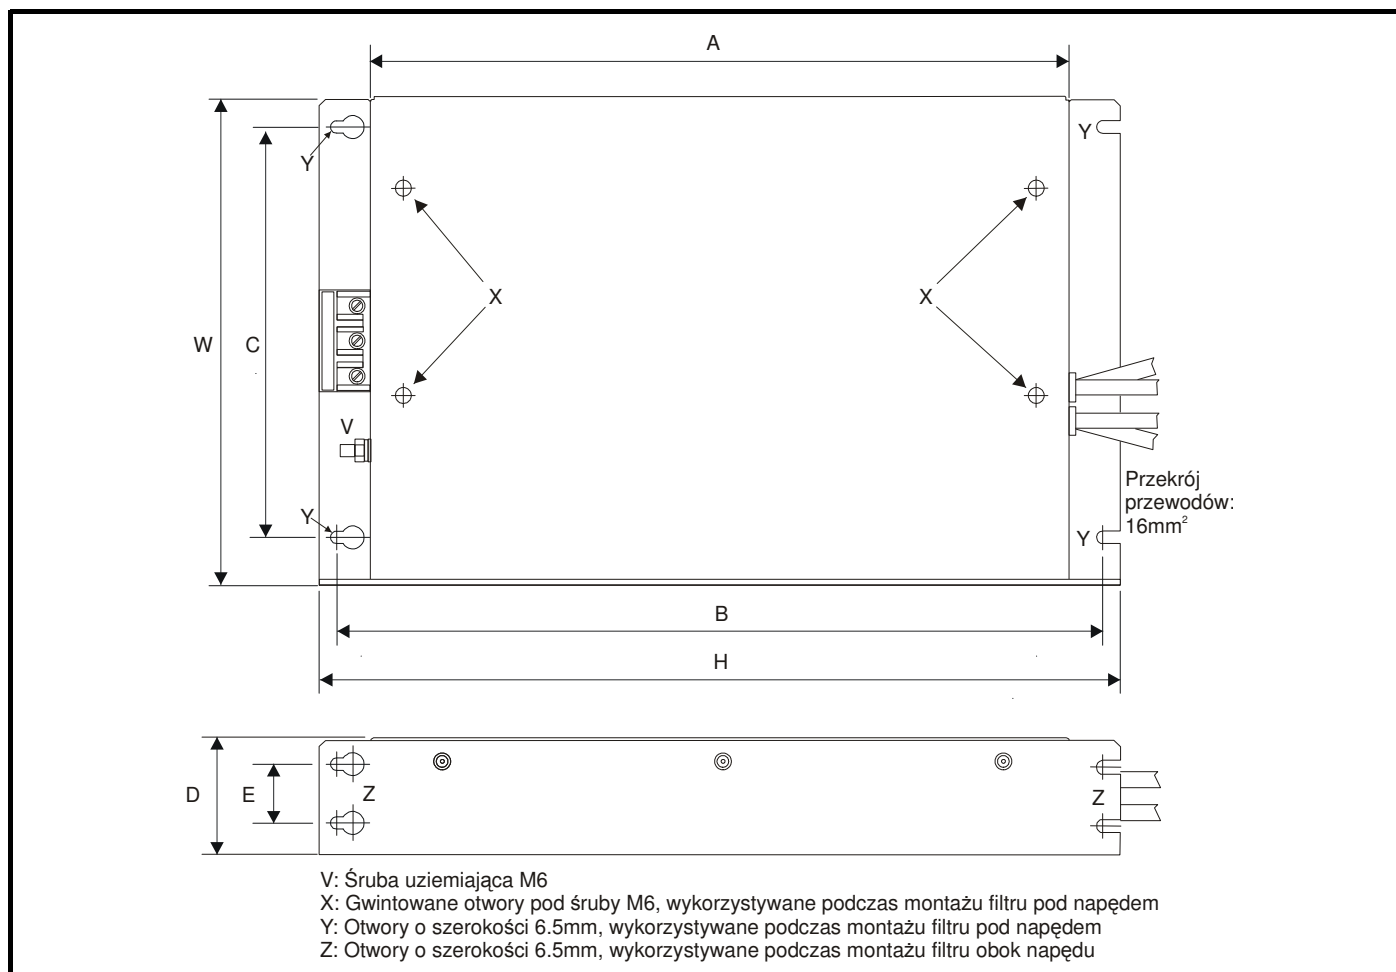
Zewnętrzny filtr EMC dla Unidrive SP Rozmiar 2
